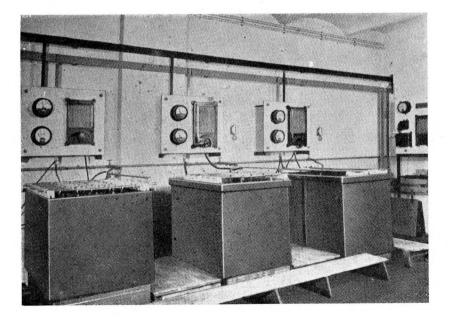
Dispositif du bain galvanoplastique Galvanic Bath with Equipment.
